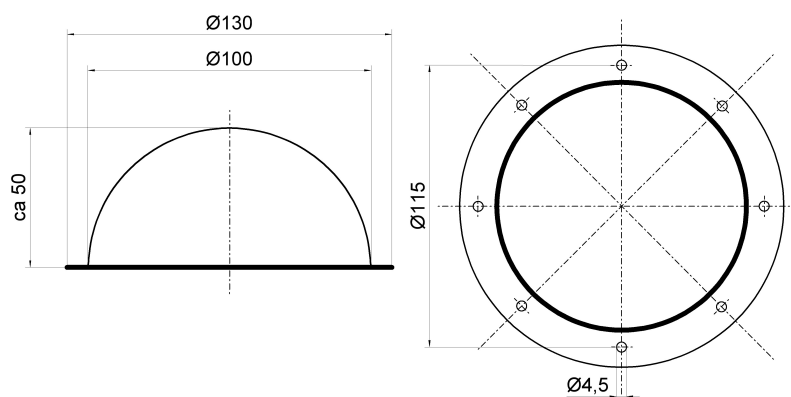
Technische Zeichnung der Acrylglas-Kuppel
